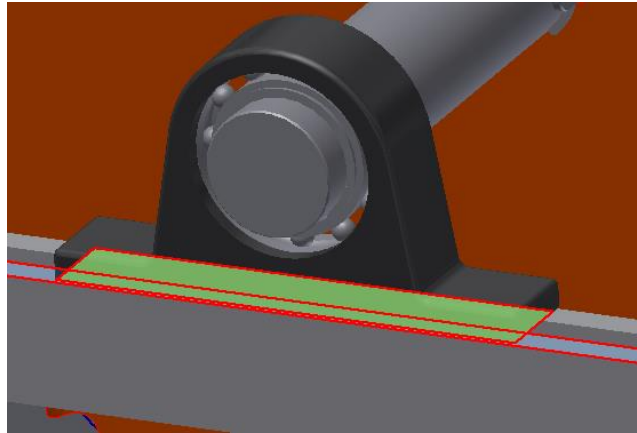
Restricción de nivelación entre las guías y el apoyo de los ejes
